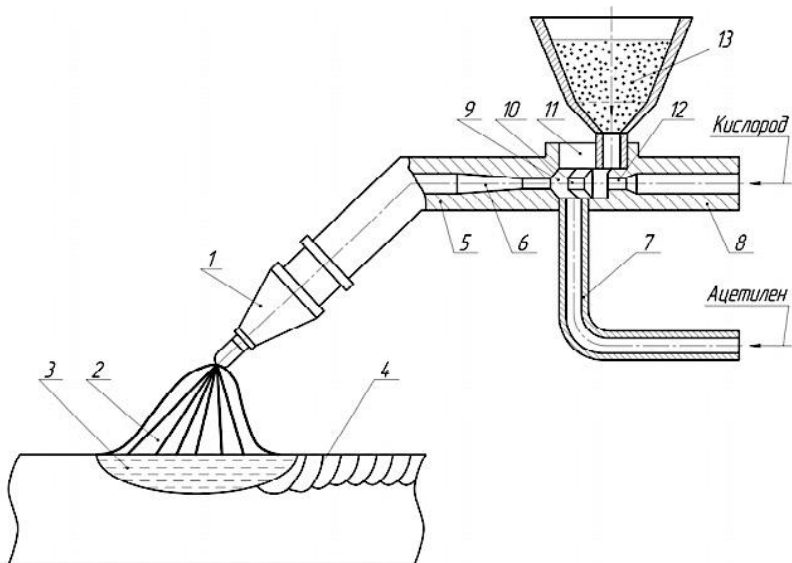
Устройство сварочной горелки [11]:
